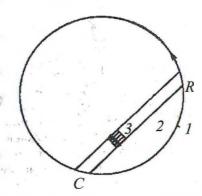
Схема процесса ротационного формования: 1 — вращающийся цилиндр; 2 — неподвижный порошок; 3 — поток скатывающегося порошка
